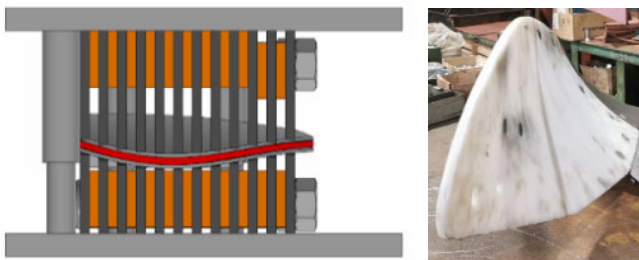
Матрица и пуансон пресс-формы для листовой штамповки термопластов (слева) и отштампованный пластиковый отвал плуга
